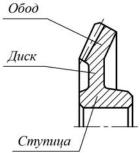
Конструктивные элементы зубчатого конического колеса
